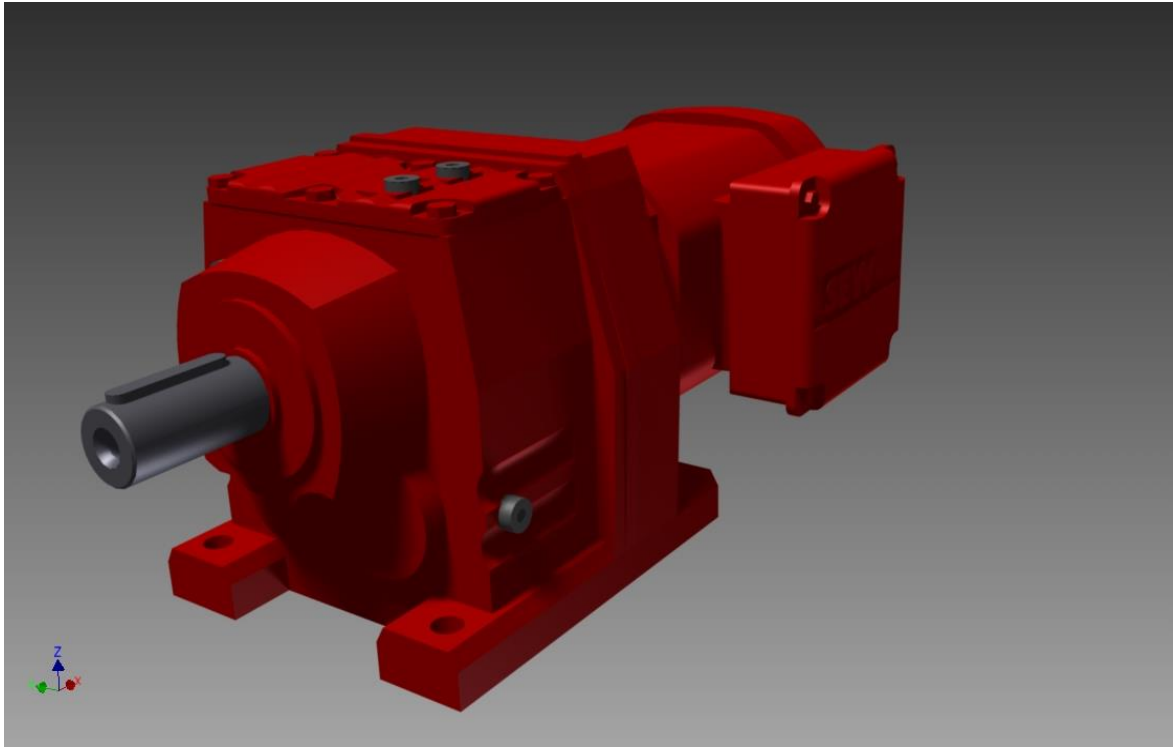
Загальний вид - мотор-редуктор SEW-EURODRIVE_ R47DRS71M4
